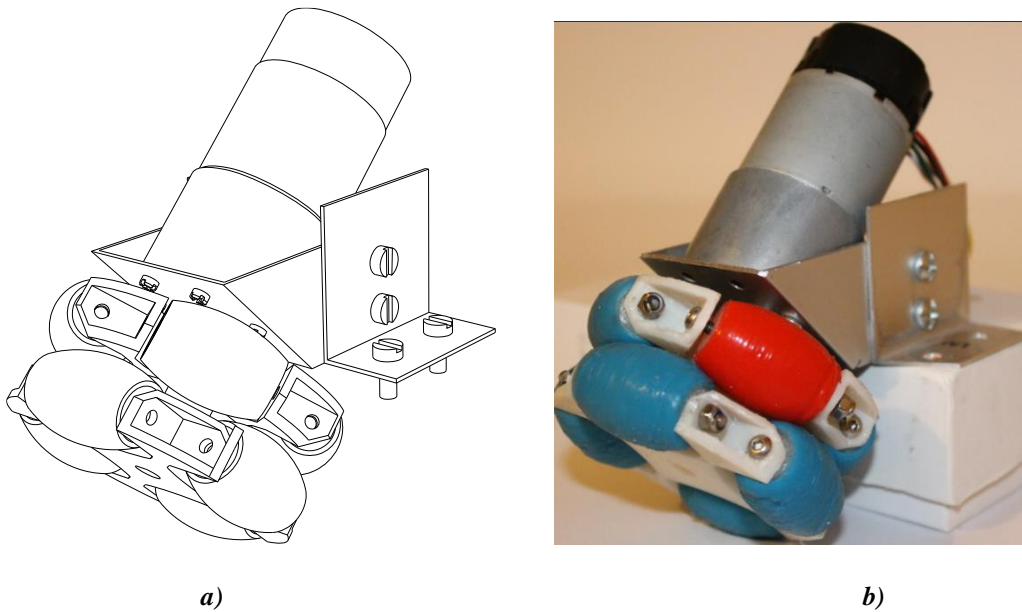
Ensamble de motor, rueda y soporte de motor. a) diseño CAD b) Construcción física.
